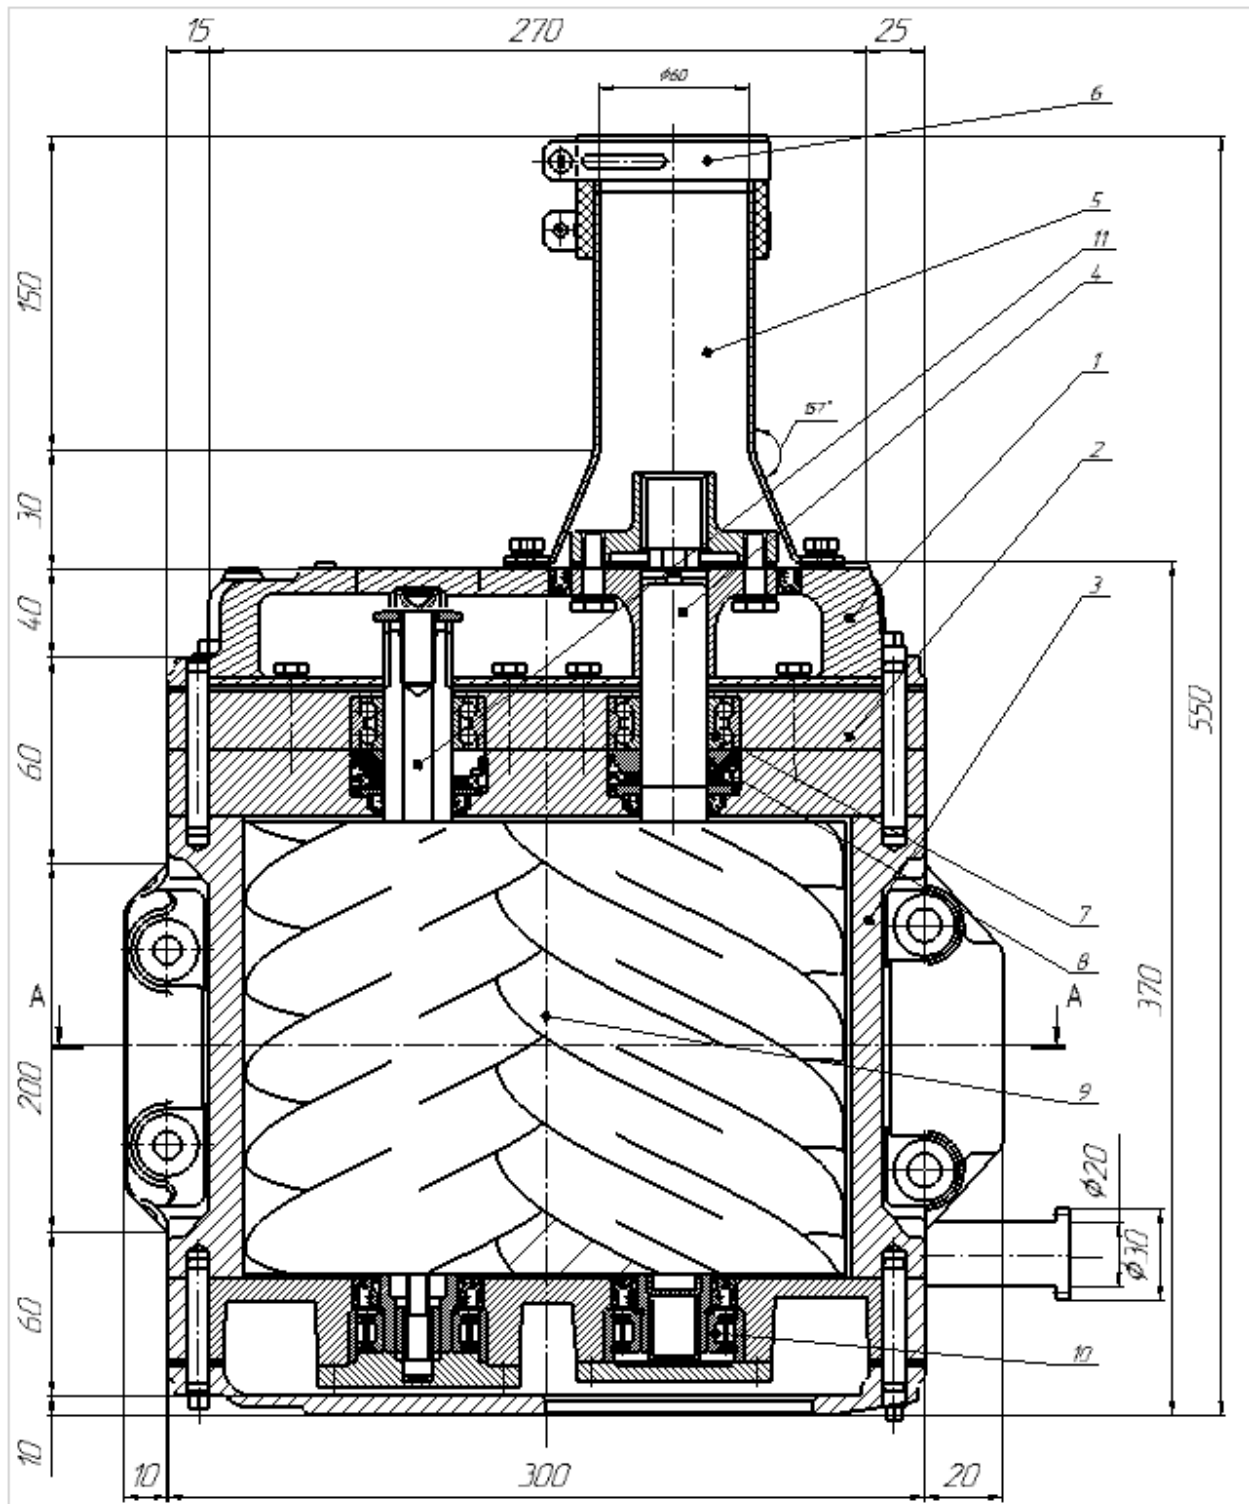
Продольный разрез винтового компрессора 2 ступени.
